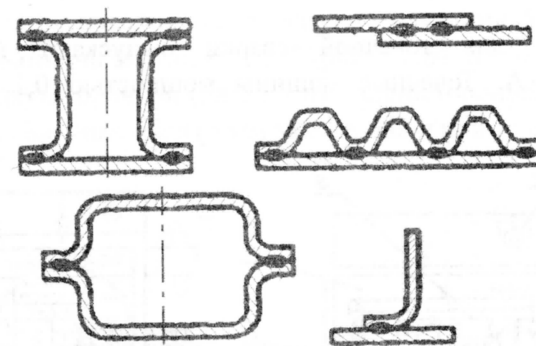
Виды соединений заготовок точечной сварки
